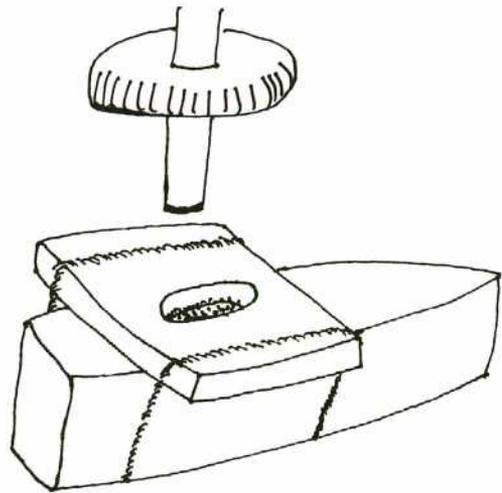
Detail der Bohreinrichtung mit dem „Schablonebrettchen“ bei einer Ovalbohrung.
